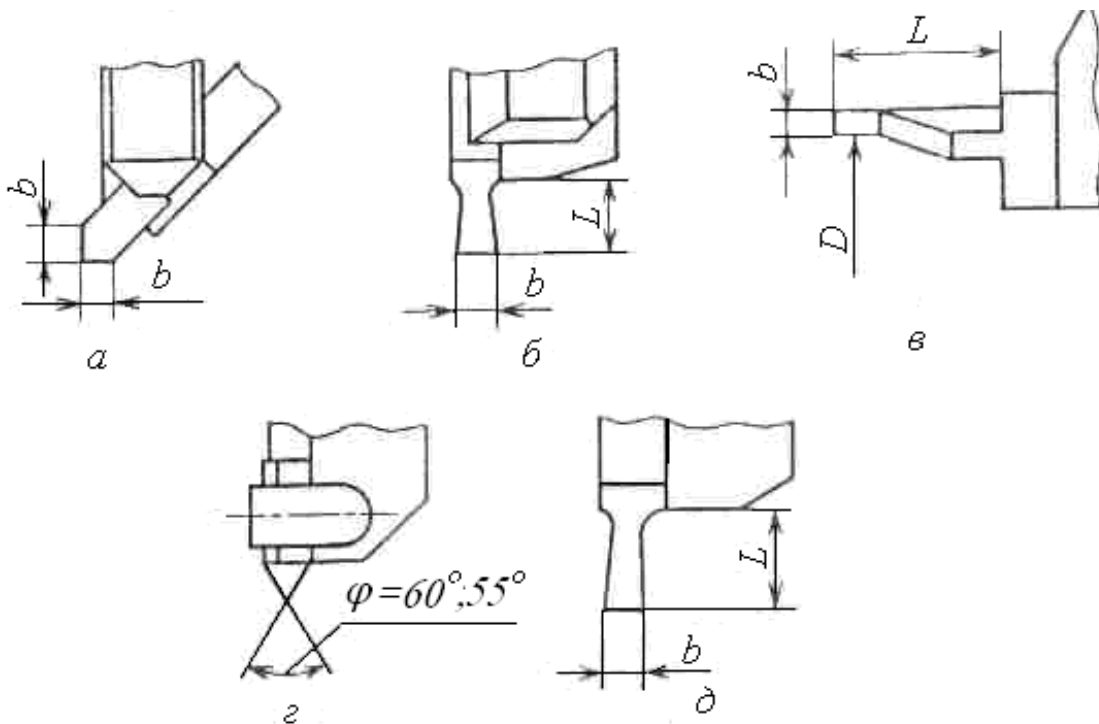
Формы резцов для обработки дополнительных поверхностей: *a* – резец канавочный угловой; *б* – канавочный; *в* – канавочный для торцовых выборок; *г* – резьбовой; *д* – отрезной
